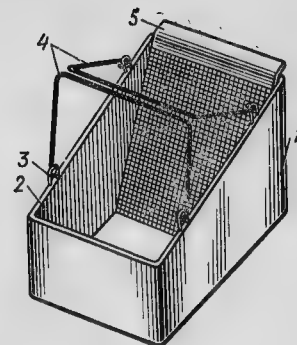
1 — корпус; 2 — отбортовка; 3 — проушина; 4 — ручки; 5 — сетка
